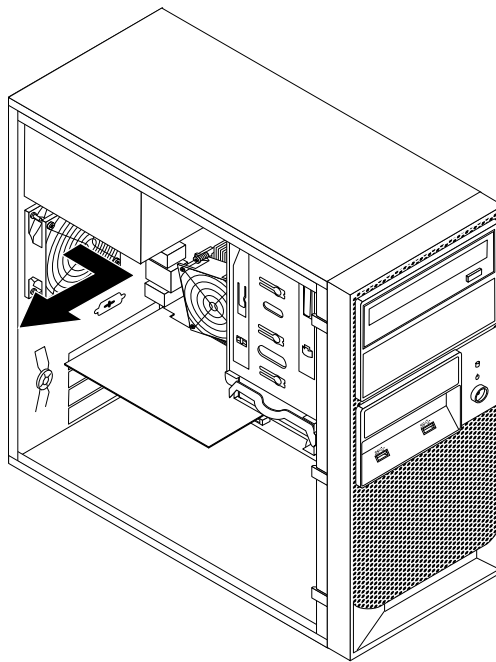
Lüftungsbaugruppe an der Rückseite entfernen
